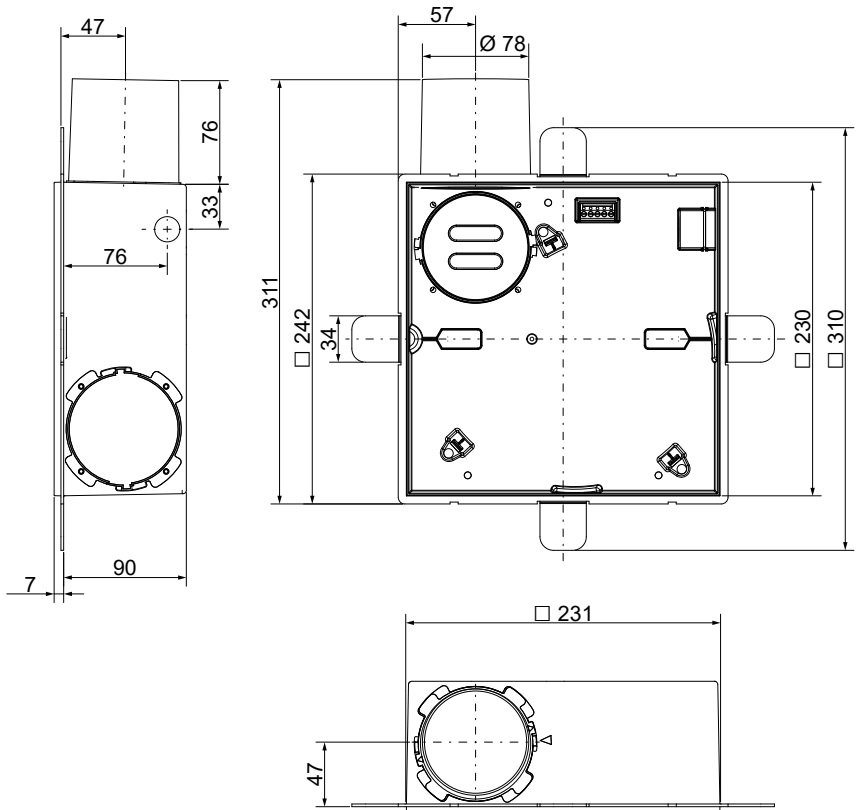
Maßzeichnung – Gehäuse Abluftventilator Taris UP radial
